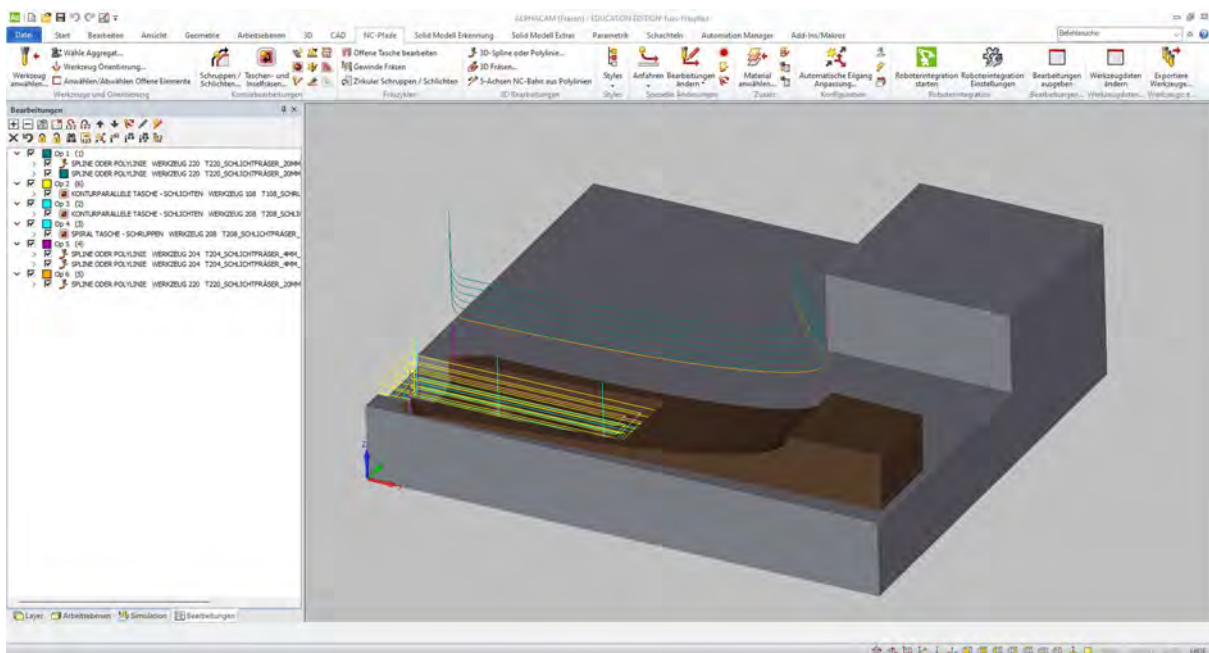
Fräsprogramm - Fuß Bearbeitung 2
